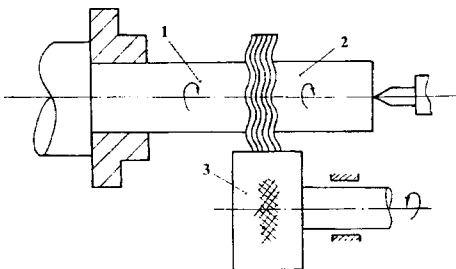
Схема приспособления для обработки гофрированных шайб до круглой формы в плане: 1, 2 – оправки; 3 – шлифовальный круг.
